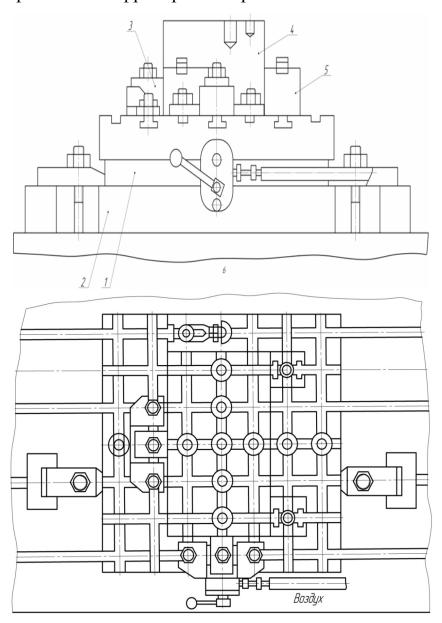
Приспособление для установки корпусной детали: 1 — пневмостол; 2 — стол станка; 3 — зажим кулачковый; 4 — заготовка; 5 — опора
